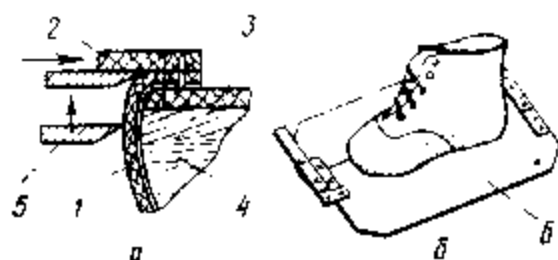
Затяжка пластинами при формировании обуви способом парко: 1 — заготовка; 2 — рант; 3 — стелька; 4 — колодка; 5 — затяжные пластины; 6 — обжимные пластины
